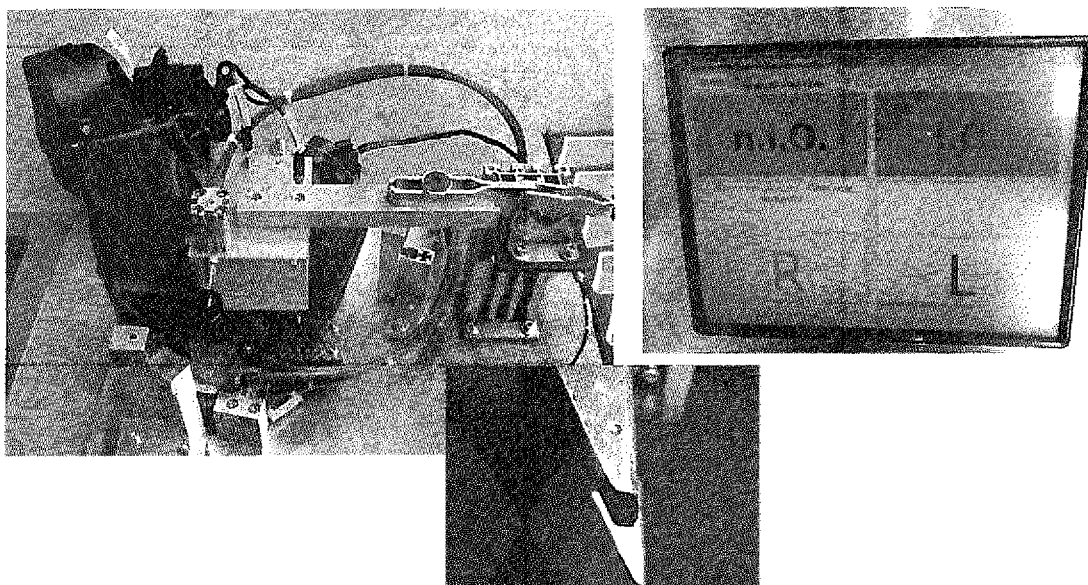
Montáž motorku a zasunutí kabelu (Zdroj: Dokumentace firmy ALFA s.r.o.)
